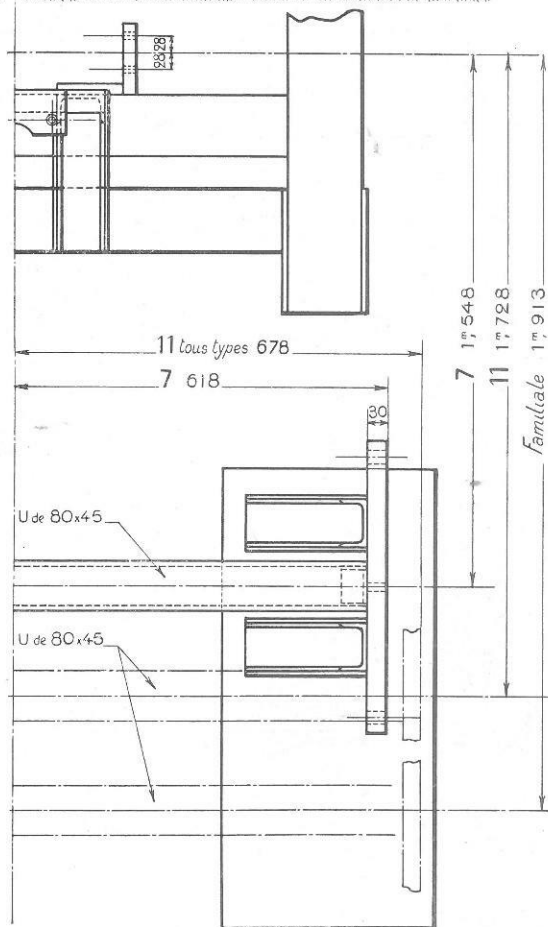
Plan de détail du montage de dégauchissage des carrosseries à traverse tubulaire.
